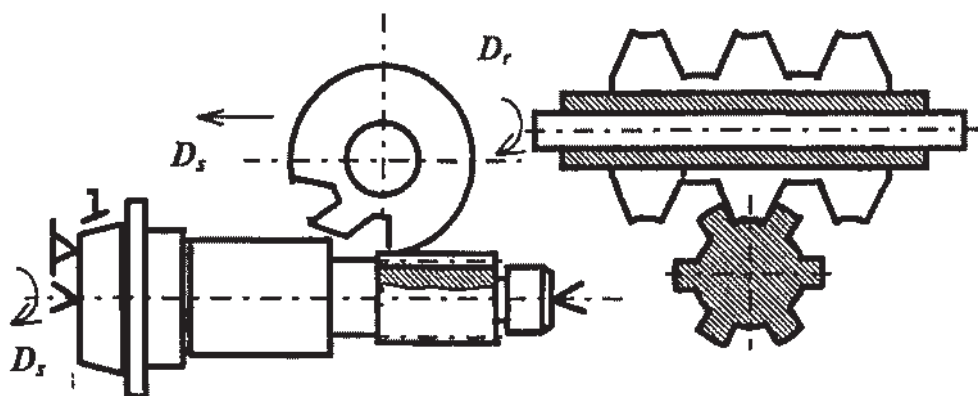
Схема обработки шлицевой поверхности на шлицефрезерном станке
